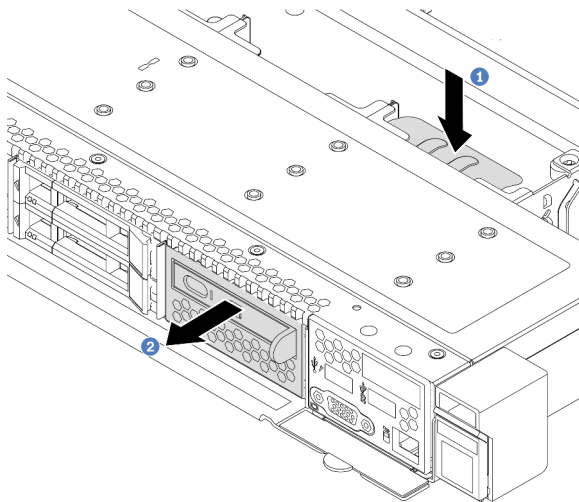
Entfernen der Baugruppe mit LCD-Diagnoseanzeige
